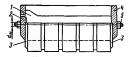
Магинтопровод статора, тый шпильками. I — ребро станины; 2 — нажимное кольцо; 3 — на-жимные пальцы; 4 — глухая стенка станины; 5— сборочные шпильки.
